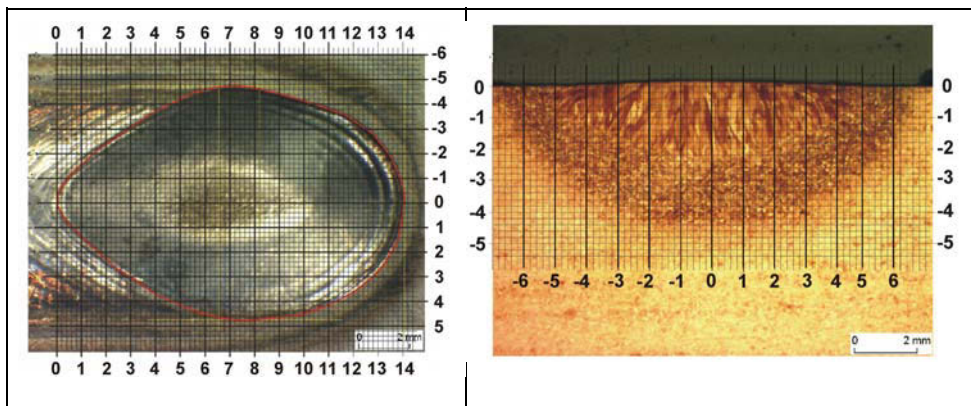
Endkrater (links) und Querschliff (rechts) einer WIG-Umschmelznäht des Werkstoffs Alloy 602 CA; Schweißparameter P1; Schutzgas: Ar + 1% N₂
